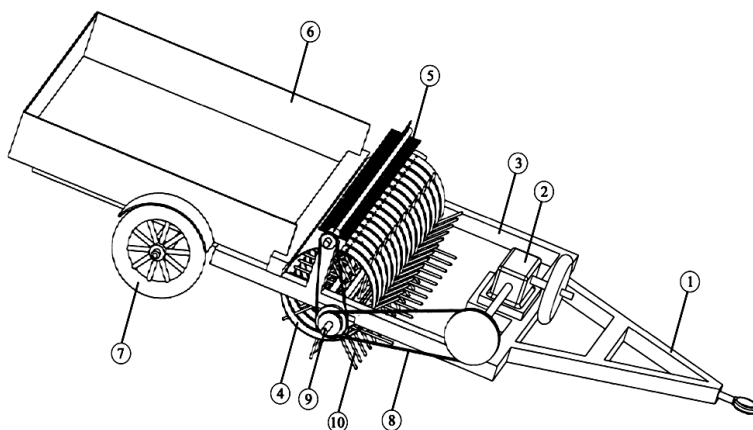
Общий вид машины «MADADKOR»: 1 - прицепное устройство; 2 - конический редуктор; 3 - рама; 4 - барабан; 5 - загрузочное приспособление; 6 - кузов; 7 - опорные колеса; 8 - ременные передачи; 9 - трубчатый (фигурный) вал; 10 - зубья
